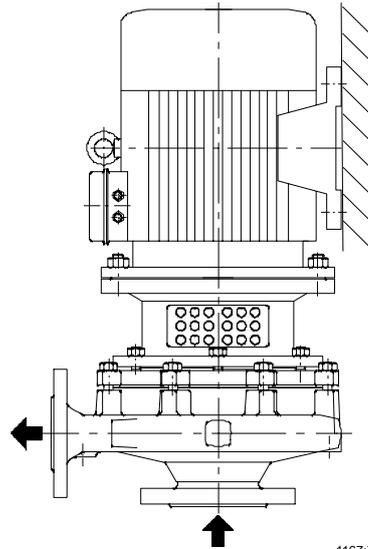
Pumpenfuß Befestigung seitlich, bis Motorgröße 112 = 4 kW
